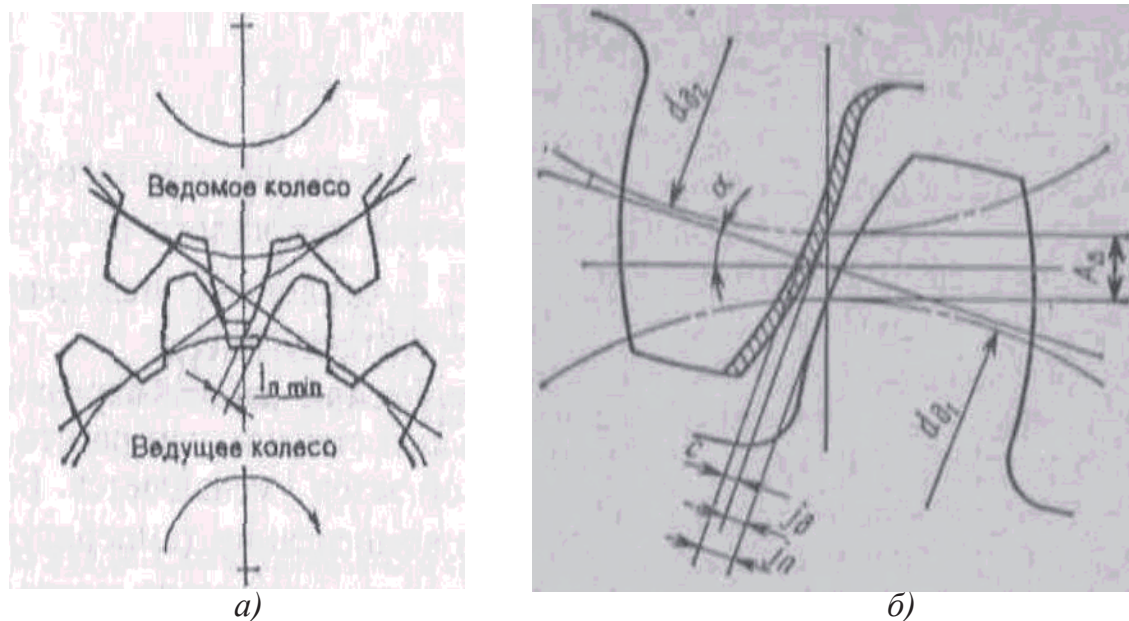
Схема образования зазора между боковыми поверхностями зубьев: *а* – схема зацепления колес; *б* – схема к определению влияния толщины зуба и смещения исходного контура на величину бокового зазора; j_n – боковой зазор; j_d – часть бокового зазора, образуемая при смещении делительных окружностей; *с* – часть бокового зазора, образуемая при изменении толщины зуба
